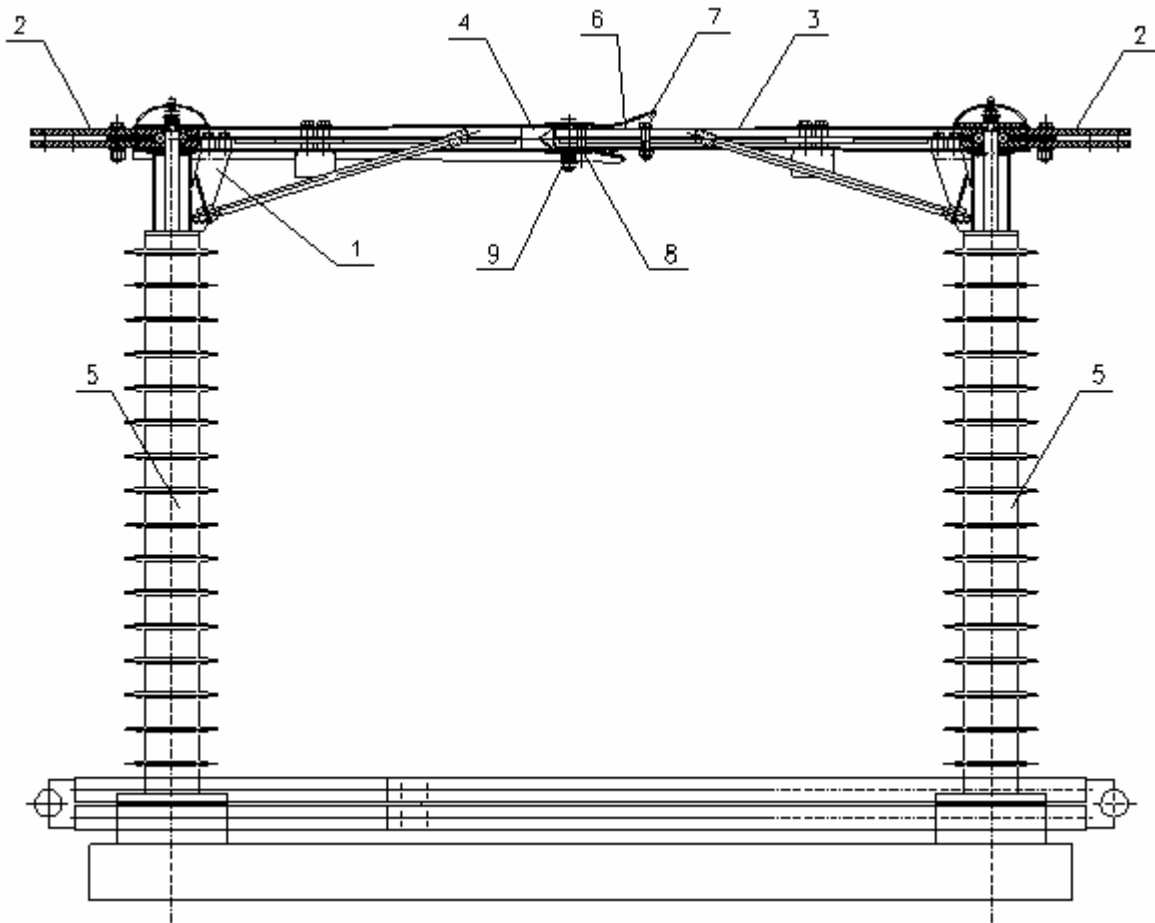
Двухколонковый горизонтально-поворотный разъединитель на 110 – 220 кВ с конструктивными средствами защиты от гололеда
